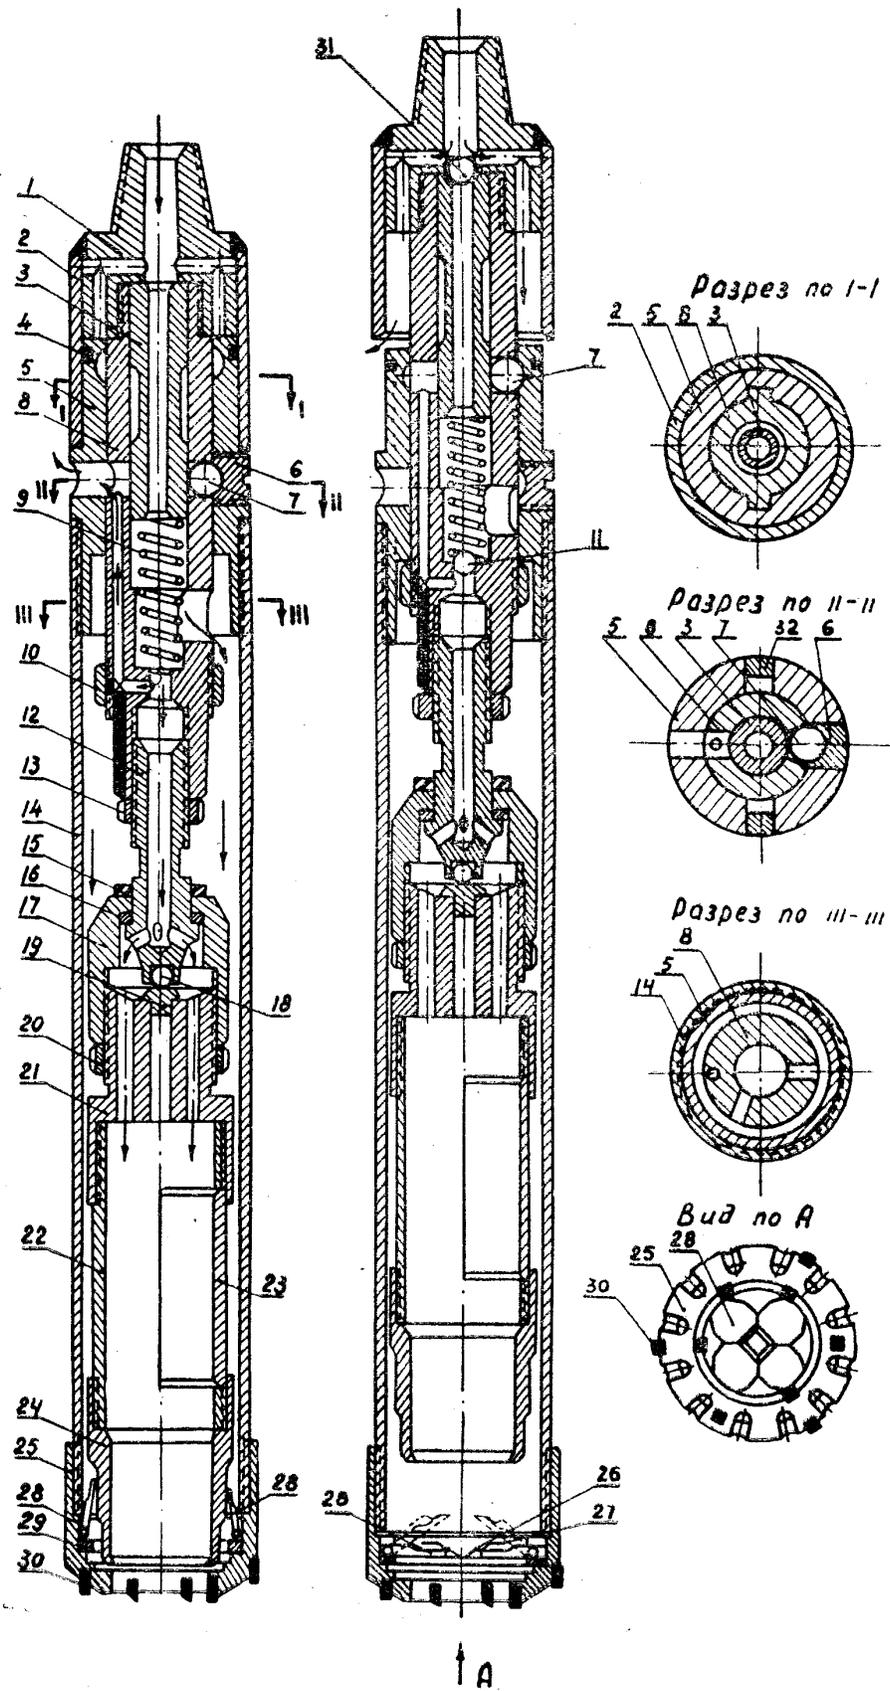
Двойной колонковый снаряд ДКС-ТПИ: 1—переходник; 2—цилиндр; 3—золотник; 4—сальник; 5—корпус; 6—пробка фиксатора; 7—шарик фиксатора; 8—шпатель; 9—пружина; 10—гайка упорная; 11—шарик для закрытия центральной промывки; 12—винт регулировочный; 13—контргайка; 14—труба наружная; 15—уплотнитель; 16—шайба; 17—корпус подпятника; 18—шарик подпятника; 19—подпятник; 20—контргайка; 21—головка керноприемника; 22—керноприемник; 23—боковая крышка керноприемника; 24—стакан приемный; 25—коронка; 26—защелка; 27—пружина кернорвателя; 28—сектор кернорвателя; 29—корпус кернорвателя; 30—резцы формы Г-1305; 31—шарик гидравлического затвора; 32—заглушка
